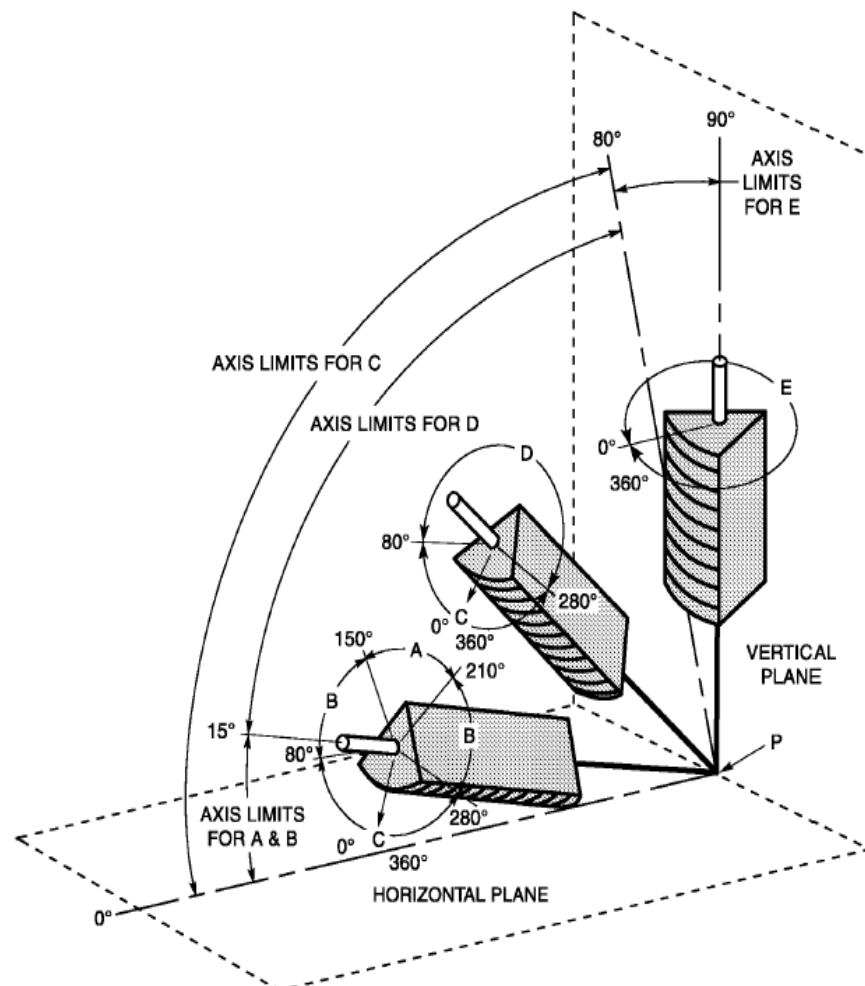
Posición del cordón de soldadura (9).
